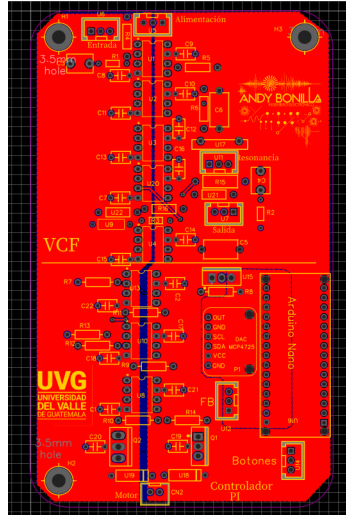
Vista 2D de PCB filtro controlado por voltaje
